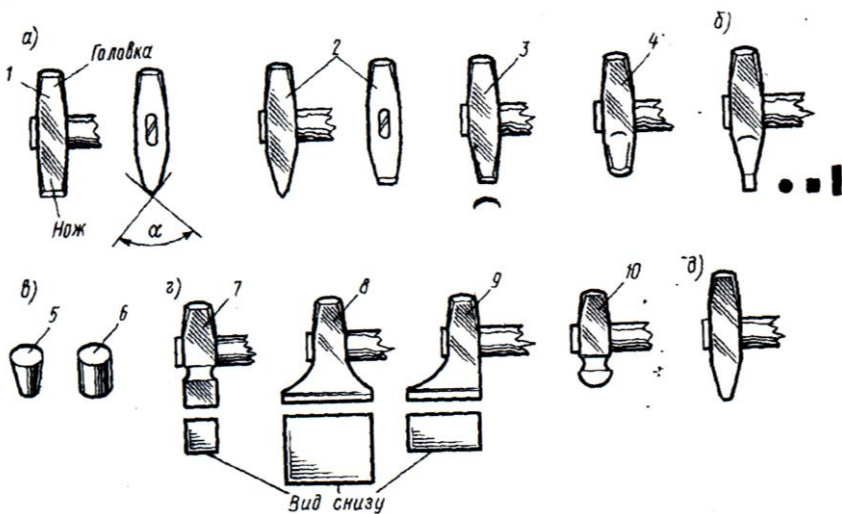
Подкладной инструмент первой группы: а - зубила (1 - для поперечной рубки; 2 - для продольной рубки; 3 - радиусные; 4 - фасонные); б - пробойник; в - прошивки (5 - конический; 6 - цилиндрический); г - гладилки (7 - с квадратной рабочей поверхностью; 8 - с увеличенной поверхностью; 9 - с односторонней прямоугольной поверхностью; 10 - с цилиндрической поверхностью); д - раскатка
